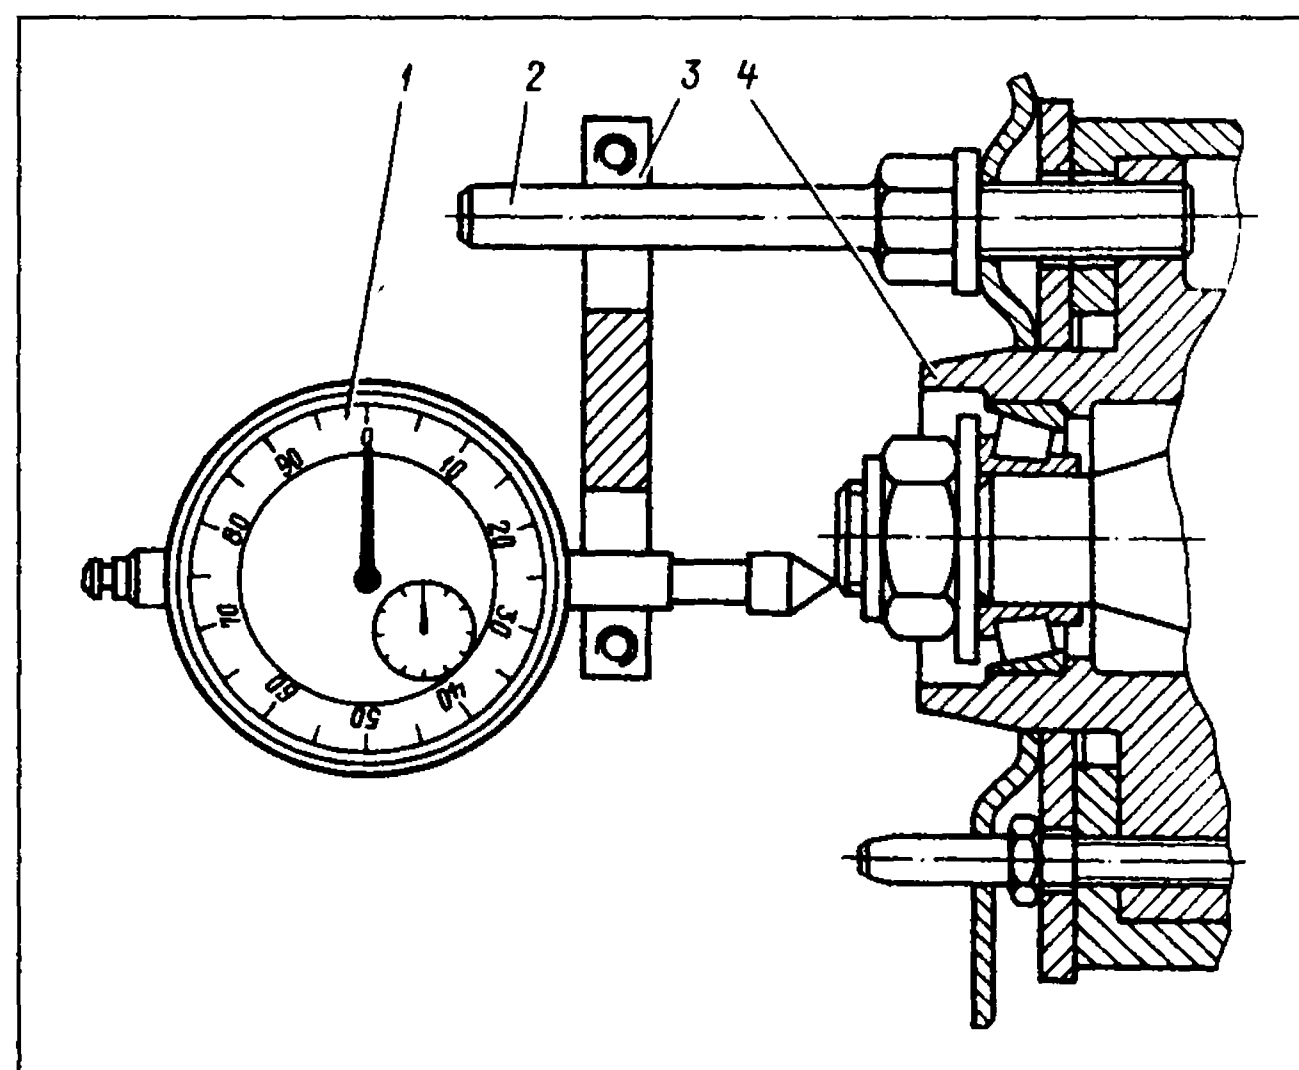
Проверка осевого зазора подшипников ступицы переднего колеса приспособлением 02.7834.9505: 1-индикатор; 2-болт; 3-кронштейн; 4-ступица
